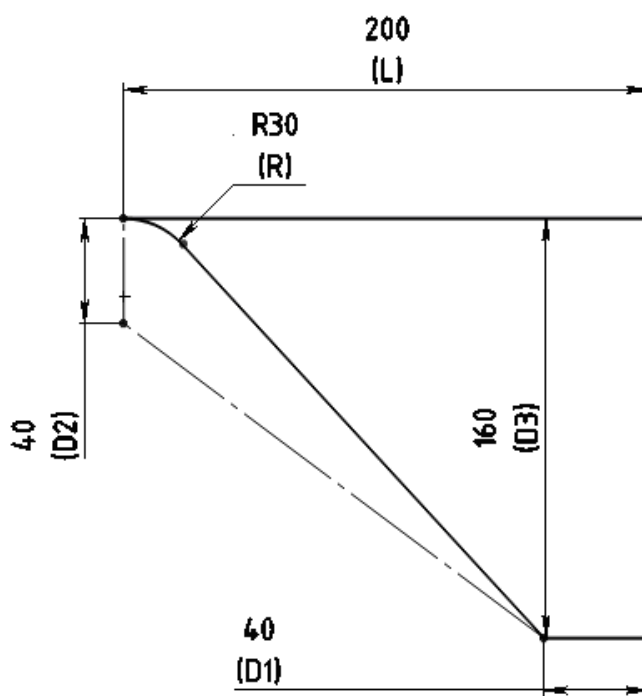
Пропонована форма косинки з обробкою після зварювання
